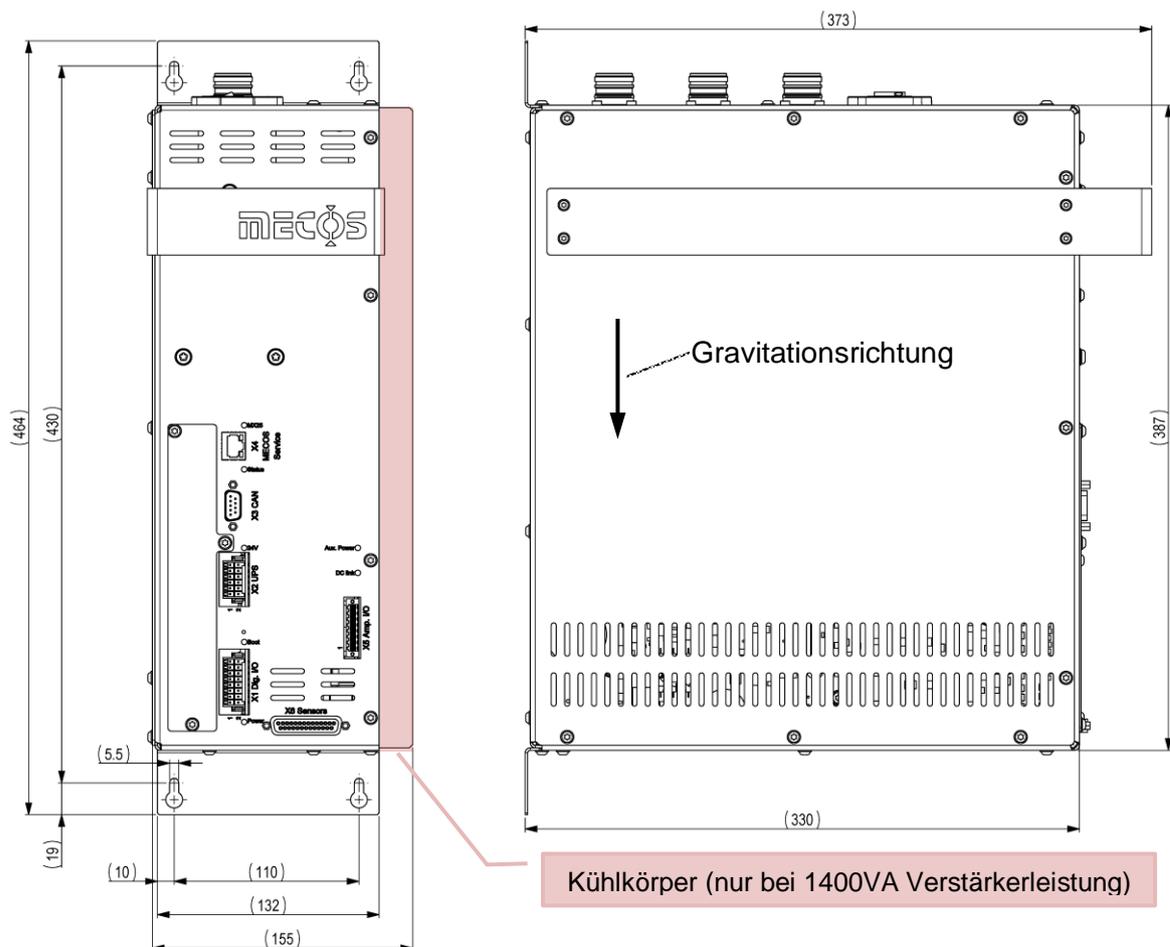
Montageansicht – Variante mit Kühlkörper, Hummel M23 Lagerstecker und D-Sub Sensorstecker
